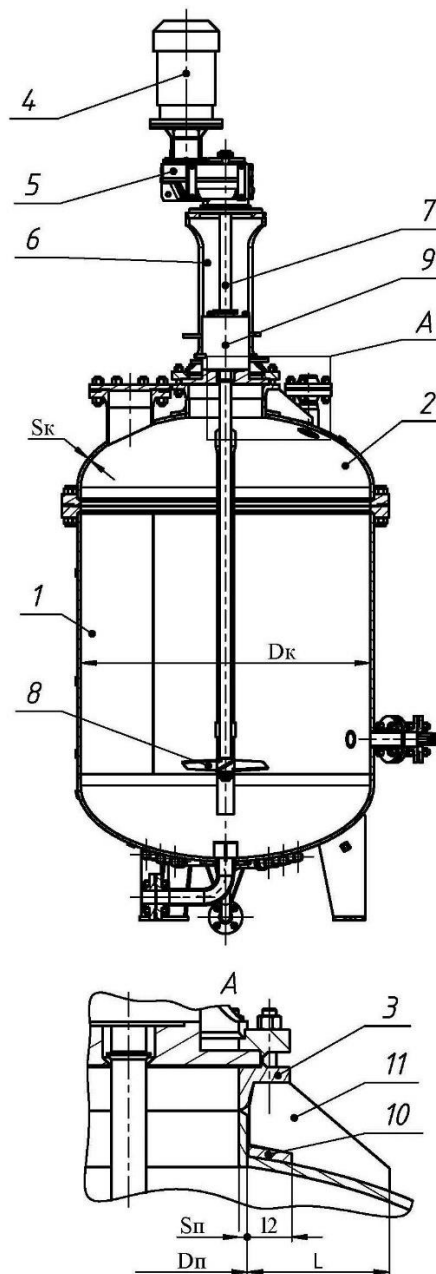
Конструкция аппарата с механическим перемешивающим устройством: 1 – корпус, 2 – крышка, 3 – штуцер под перемешивающее устройство, 4 – электродвигатель, 5 – редуктор, 6 – стойка, 7 – вал, 8 – мешалка, 9 – уплотнение, 10 – кольцо укрепляющее, 11 – ребро
